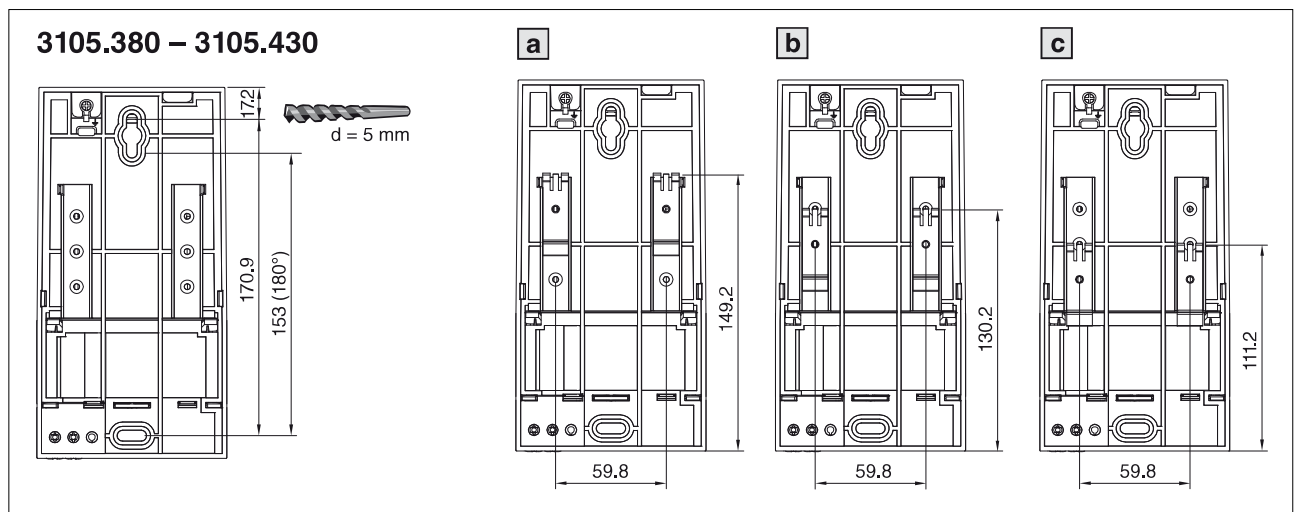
Fixation sur plaque de montage / Possibilités de fixation sur rail porteur
